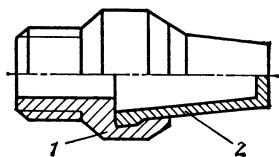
Металлокерамический глушитель типа ГМ1 (1 — штуцер; 2 — металлокерамический стакан)
